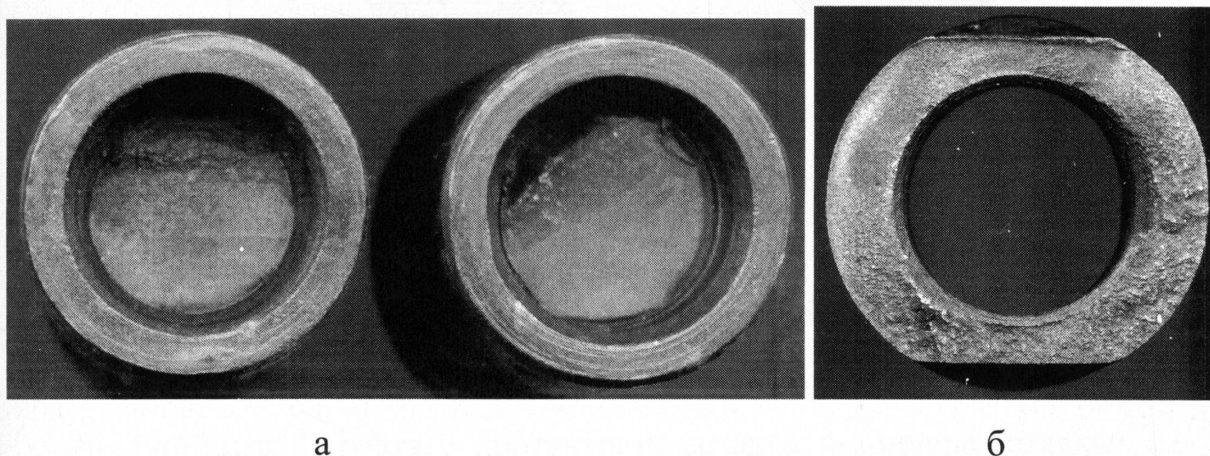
Типові корозійно-втомні руйнування муфтового різьбового з'єднання насосних штанг: а – по першому витку різьби ніпеля; б – по останньому робочому витку різьби муфти
